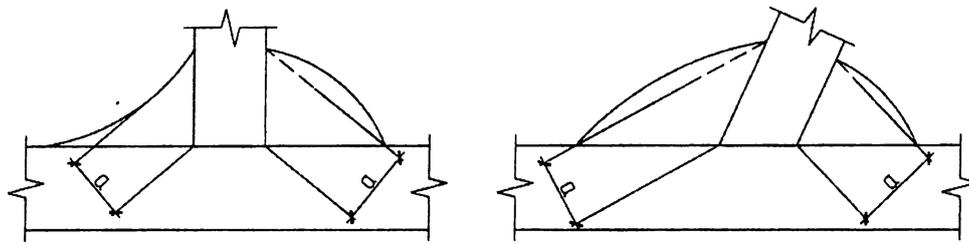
(рис. 4.3 [38]) – Эффективная толщина углового сварного шва
